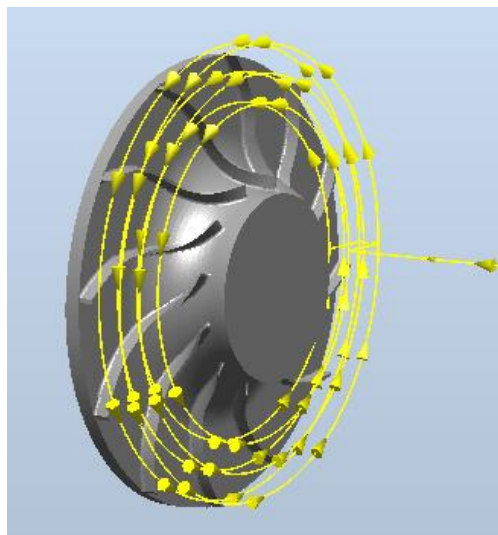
Rotina de desbaste para a maquinagem do rotor.
